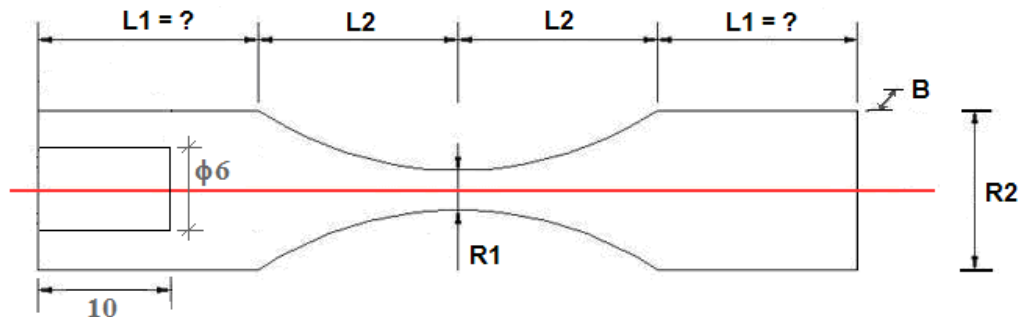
Plan de l'éprouvette de fatigue ultrasonique plate
